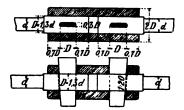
u. 175. Verlängerung von Rundeisen mittels Keilverbindung.
